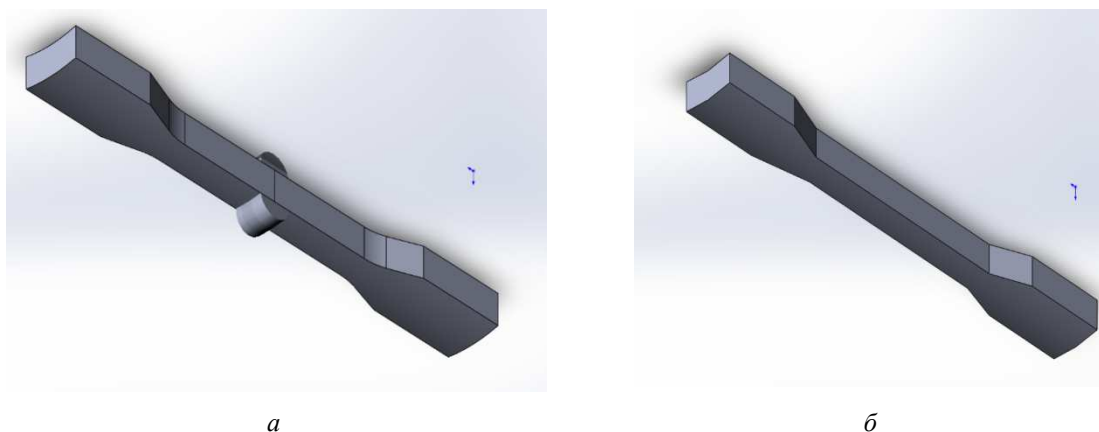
Модели образцов I типа: а – модель образца I типа из сварного стыка;
